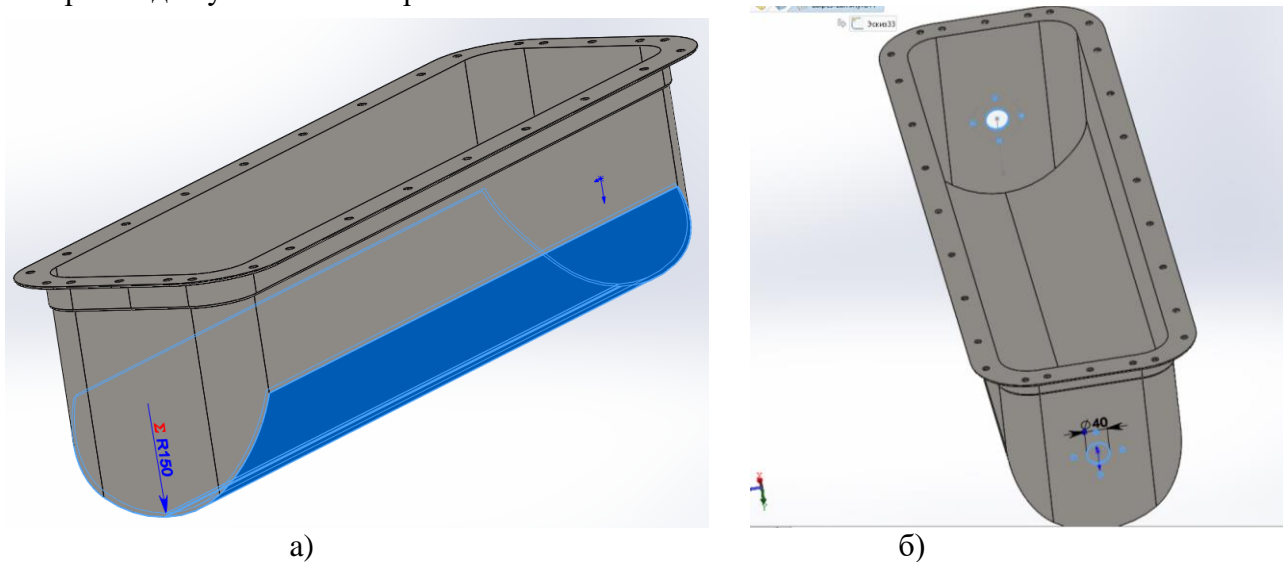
Построение скругления (а) и отверстий для установки опор (б) в корпусе шнека
